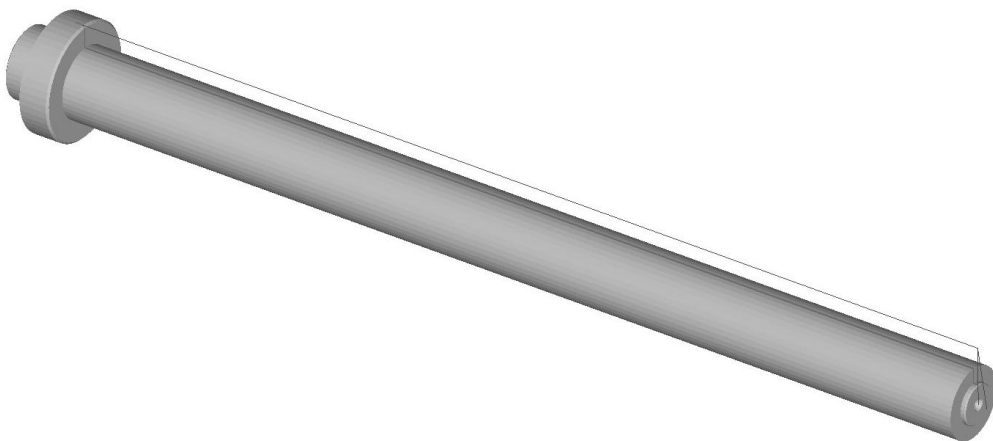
Рух інструменту при обробці правої сторони деталі «Вал»
